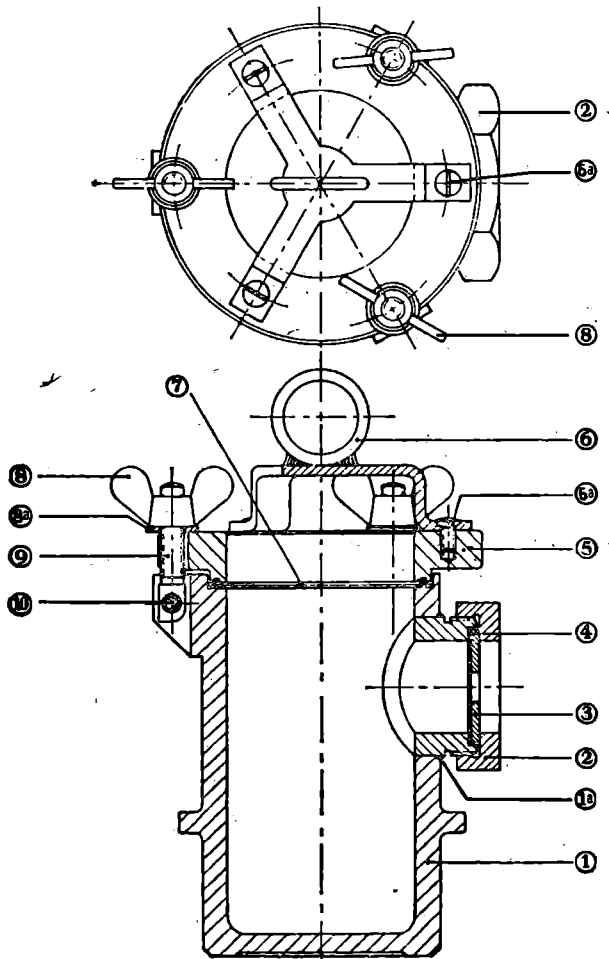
Recipiente a presión montado (vistas esquemáticas en sección vertical y en planta)
